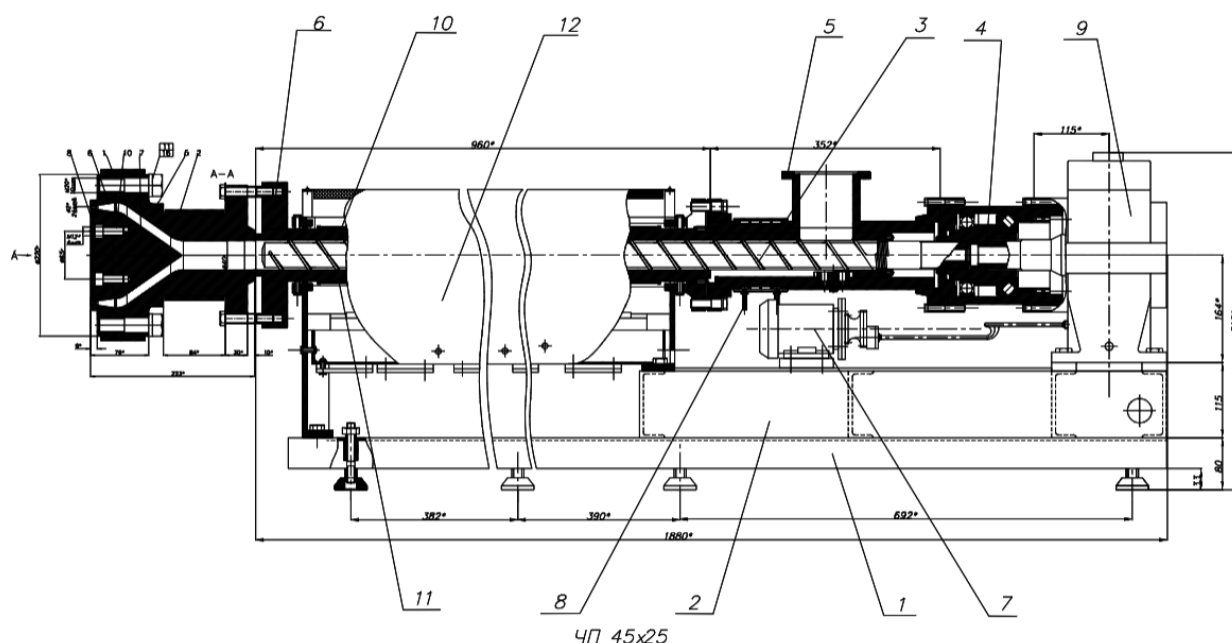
Принципова схема одночерв’ячного екструдера: 1 – рама (станина); 2 – кожух станини; 3 – завантажувальний патрубок; 4 – підшипниковий вузол; 5 – завантажувальна лійка; 6 – фланцеве з’єднання головки; 7 – система змащення (насос); 8 – нагрівники; 9 – редуктор (привід); 10 – черв’як (шнек); 11 – циліндр; 12 – кожух термоізоляції
